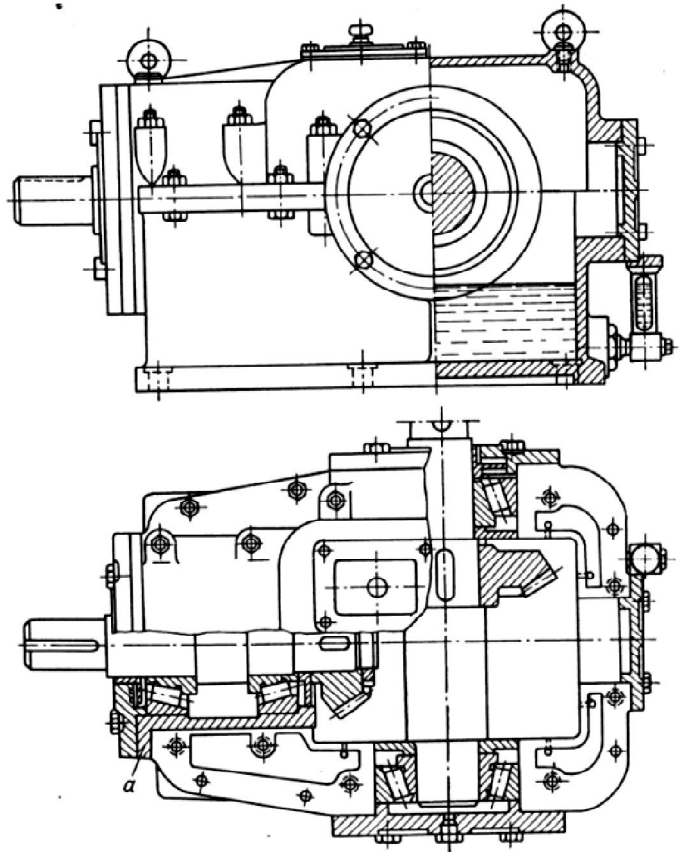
reductor de engranajes cónicos (Ref.1)
